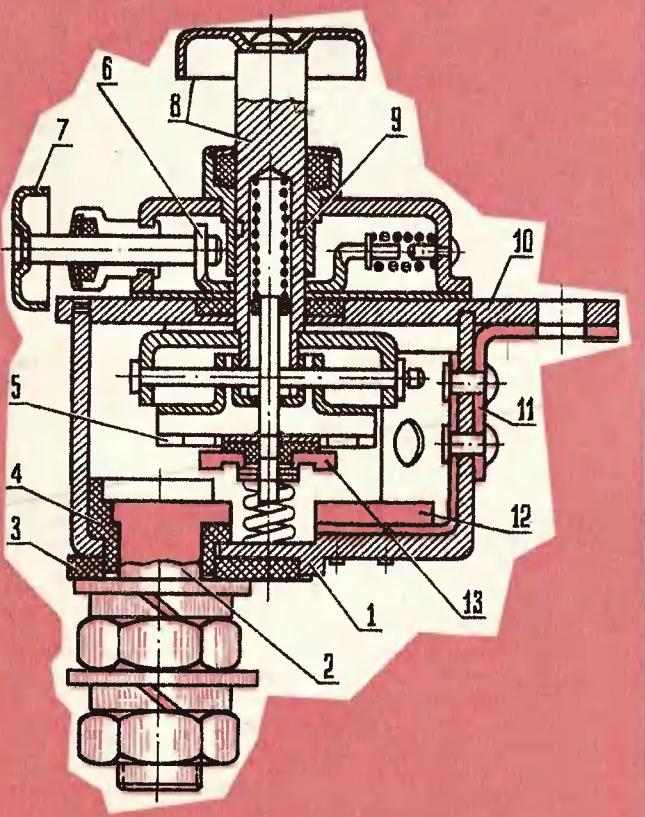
Выключатель массы ВК-318: 1 — корпус; 2 — выводной болт; 3 — изоляционная шайба; 4 — изоляционная втулка; 5 — подвижный контакт; 6 — чека; 7 — кнопка выключения; 8 — шток с кнопкой включения; 9 — вырез; 10 — крышка; 11 — шина; 12 — массовый контакт; 13 — феронконтакт.
